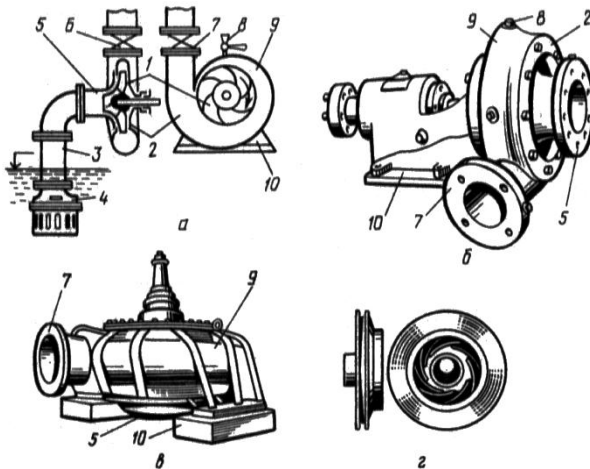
Відцентрові насоси (Ерхов М.С., Льїн М.І, Місєнев В.С., 1991): а – схема, що пояснює принцип дії; б, в – зовнішній вигляд; з – робоче колесо; 1 – лопать робочого колеса; 2 – корпус; 3 – всмоктуючий трубопровід; 4 – приймальний клапан з сіткою; 5 – кришка корпусу з всмоктуючим патрубком; 6 – засувка; 7 – напірний патрубок; 8 – пробка отвору для заповнення корпусу насоса водою; 9 – равлик; 10 – опора.
